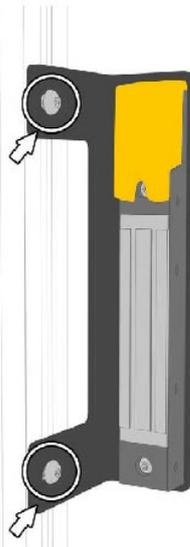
Montageplatte mit Prozesszuhaltung am Profil anbringen und und Schrauben M8 x 12 mm Torx festziehen.
